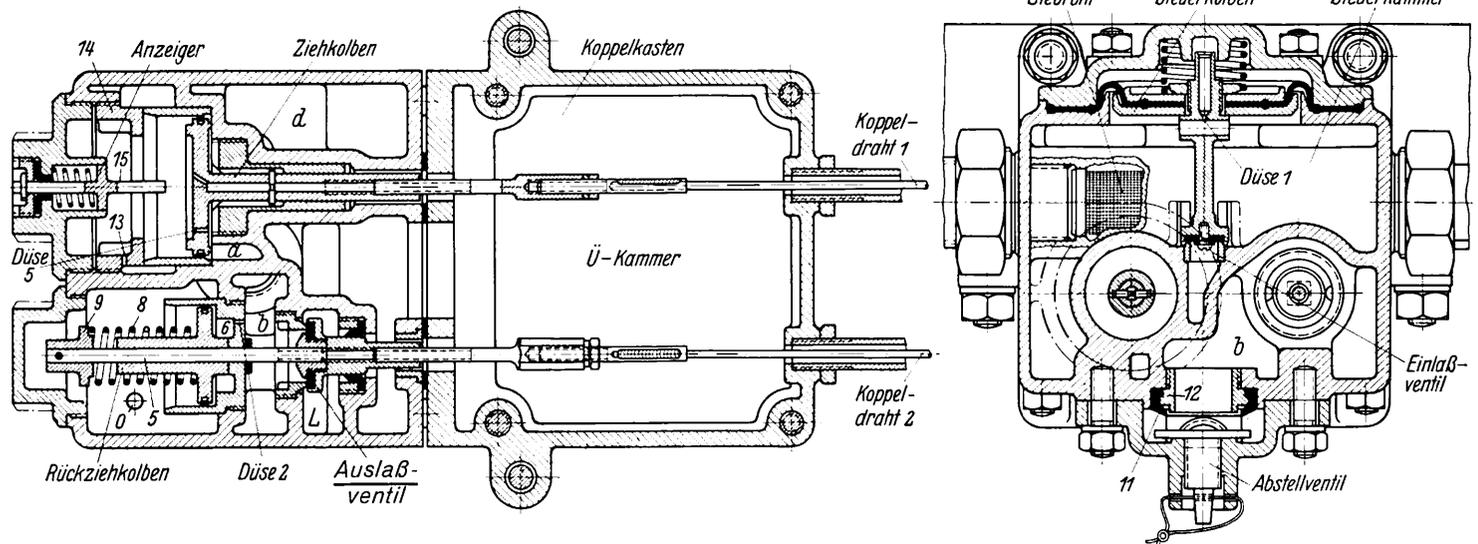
Gekoppelter Beschleuniger E mit Koppelkasten.
